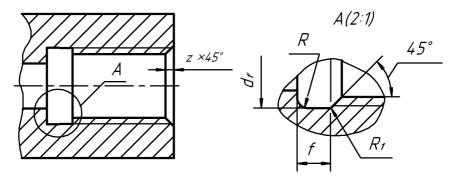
Проточка и фаска внутренней метрической резьбы
